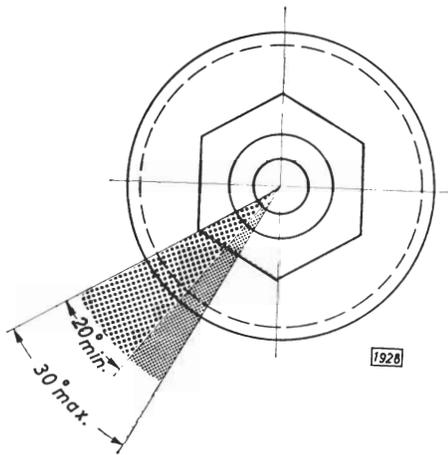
Einstellschraube 20° bis 30° zurückdrehen (30° entsprechen 1/12 Umdrehung)
